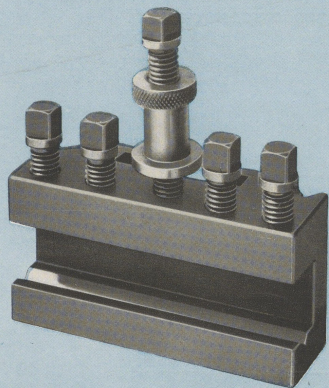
Werkzeughalter mit V-förmiger Auflagefläche für Stähle mit rundem Querschnitt.
